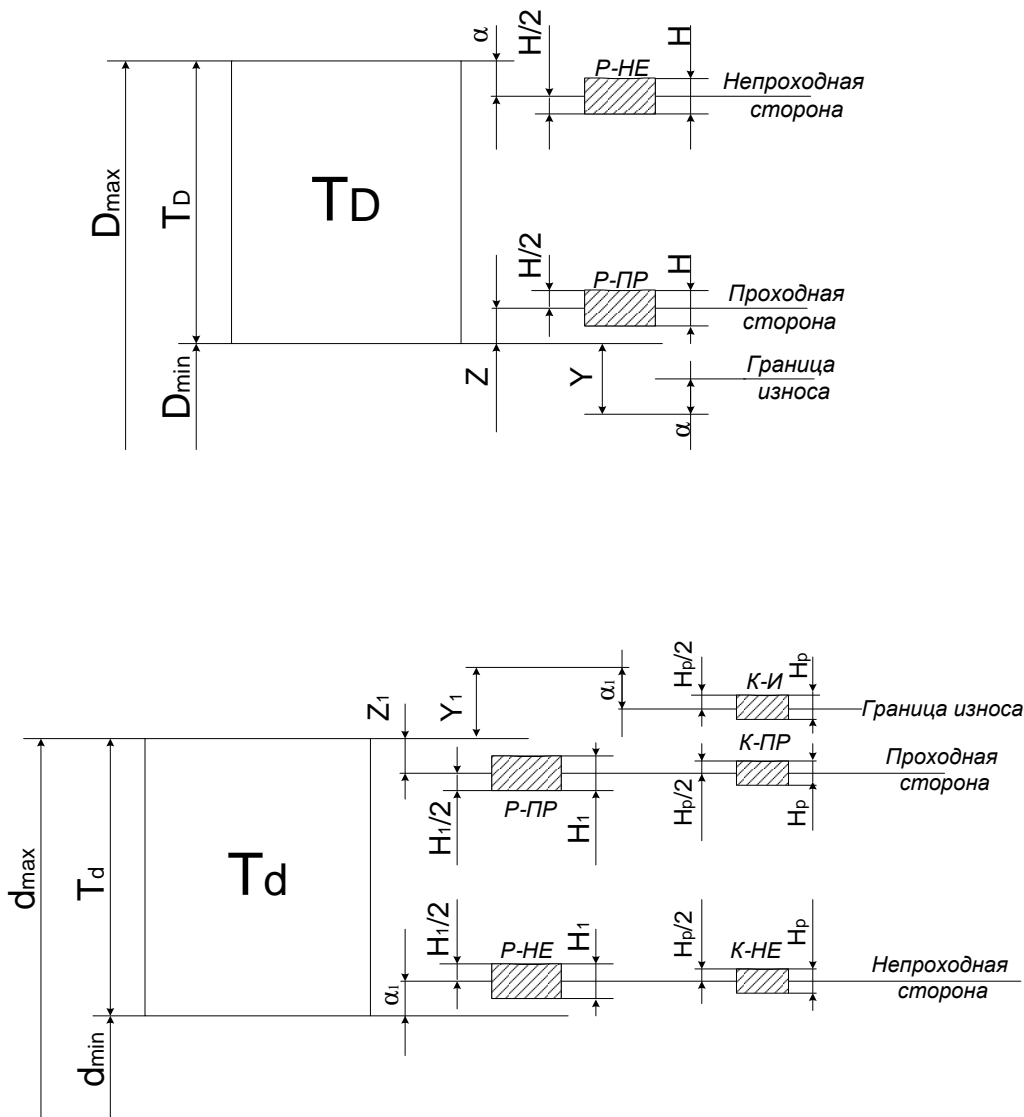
Схемы расположения полей допусков калибров
